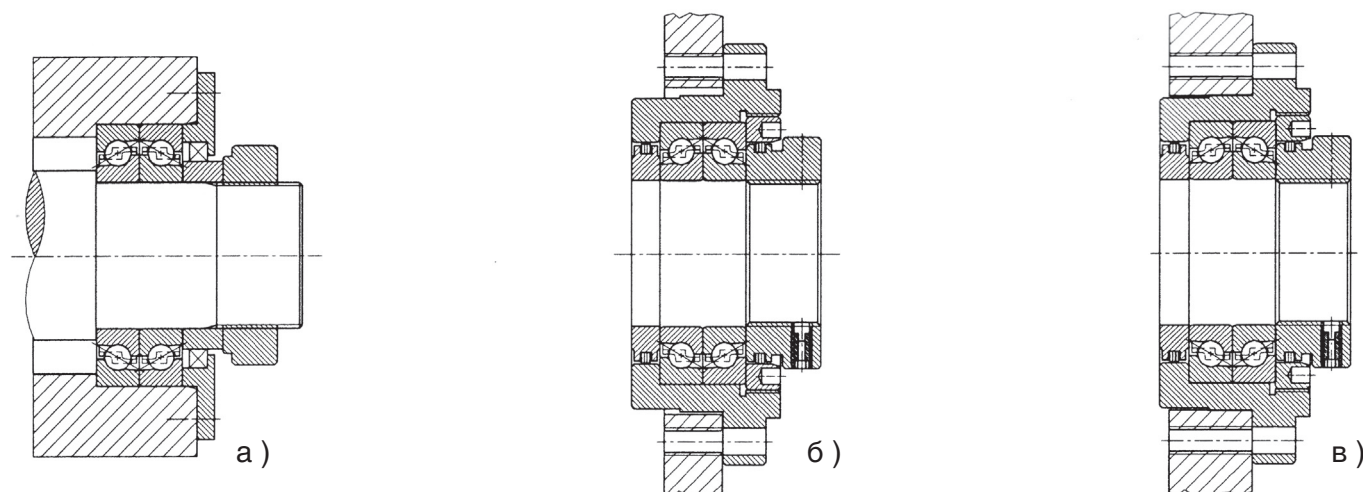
Разработка удобных для изготовления и монтажа опор обкатных винтовых передач.
